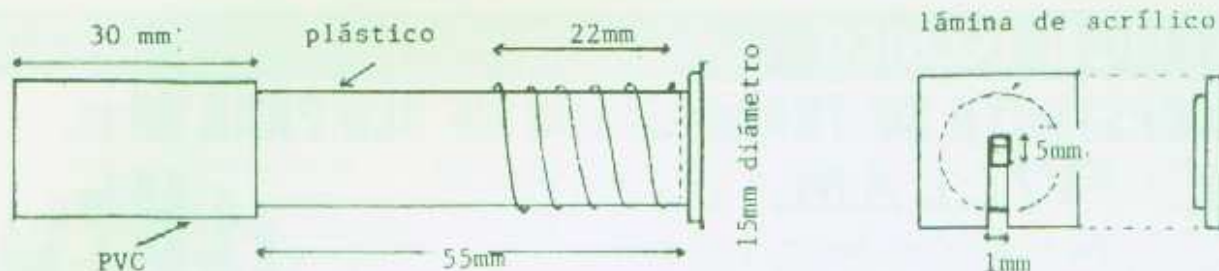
a) Detalle constructivo de la bobina L1; b) La lámina de acrílico va pegada en el caño plástico para apoyar el fleje del ferrite.
